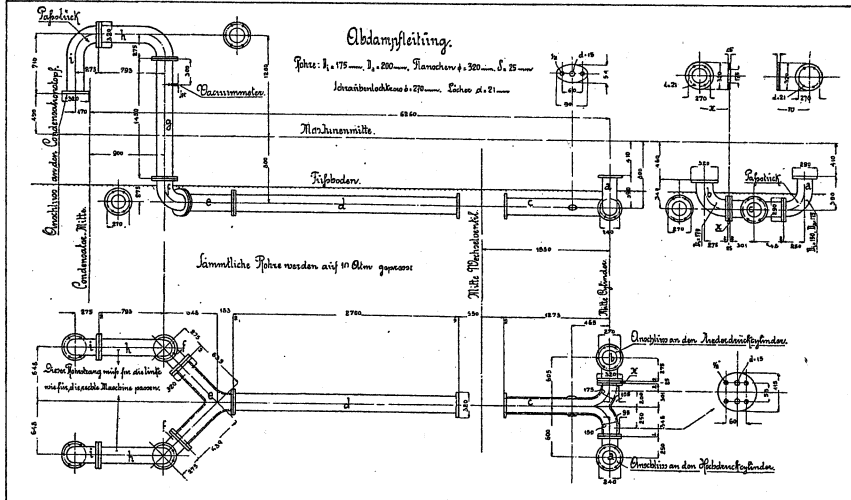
/4: Detaillierter Rohrleitungsplan (um 1890)
